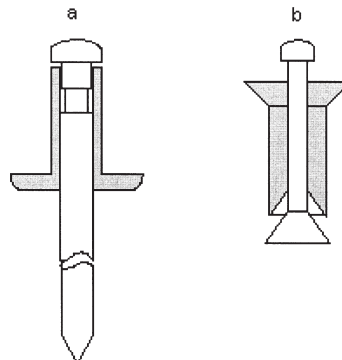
Exemple de rivet; a) rivet aveugle, b) écrou à sertir
